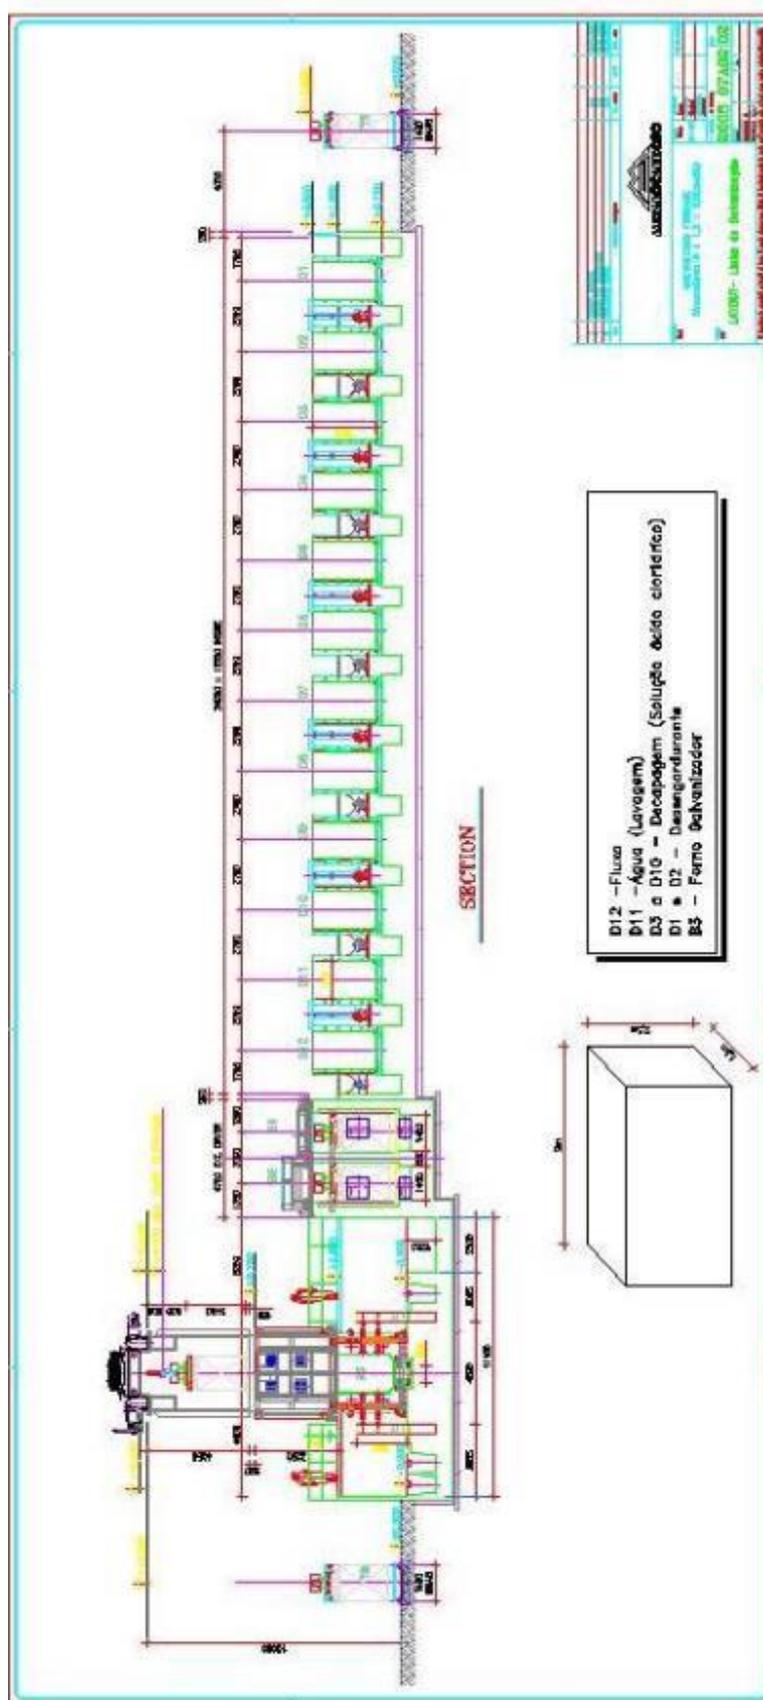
Planta de implantação da linha de galvanização da METALCARDOSO.
